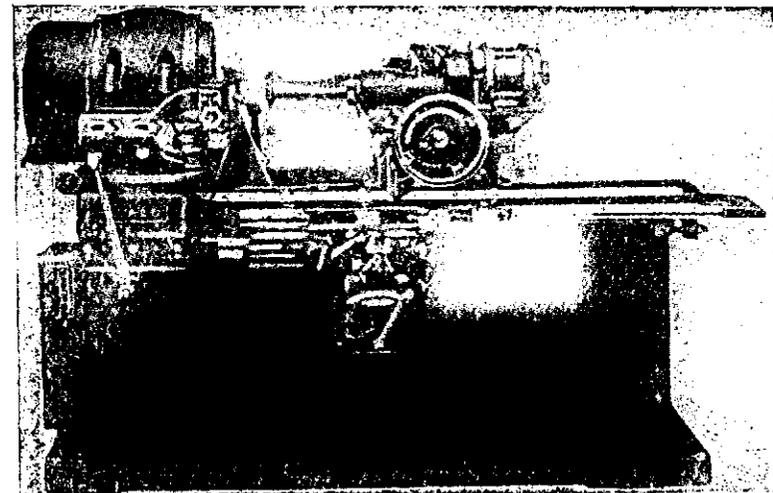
Шлифовальный станок фирмы „Хильд“ для шлифовки зеркала цилиндра.
